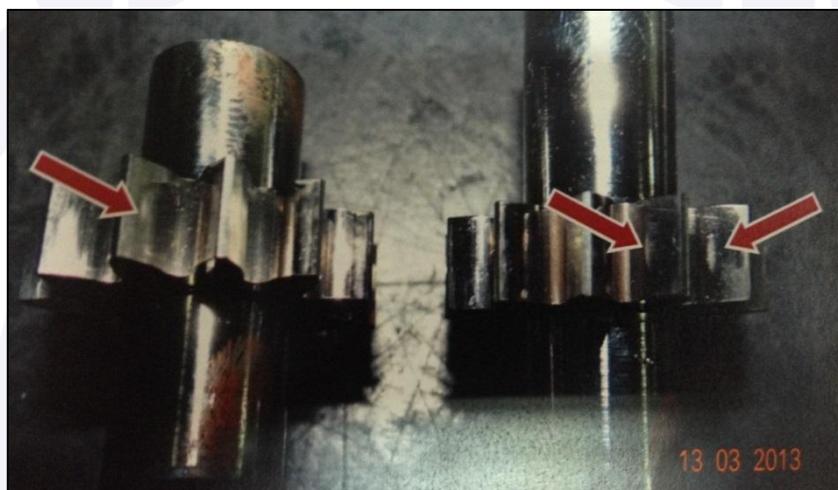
Vista geral das engrenagens da bomba de combustível com indício de cavitação.
